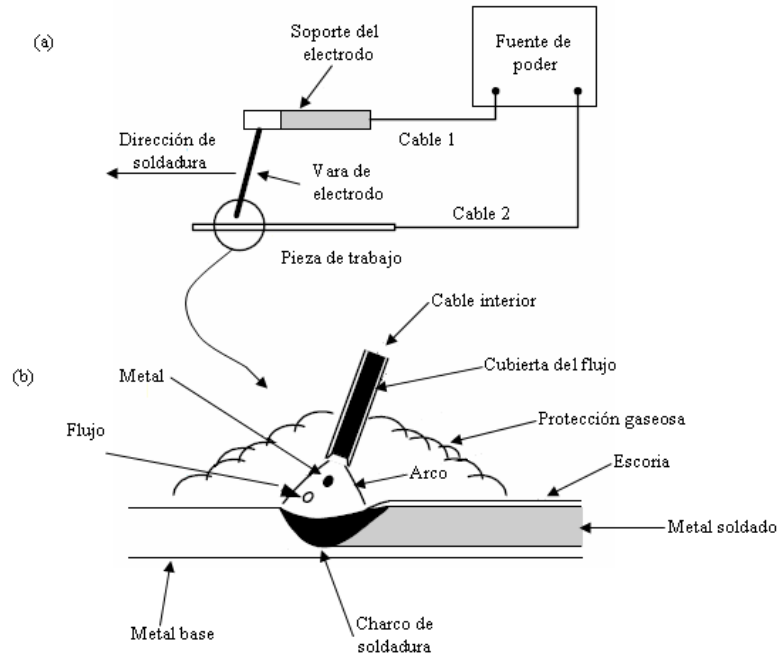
Soldadura MMA: (a) proceso total y (b) área de soldadura alargada [1].
